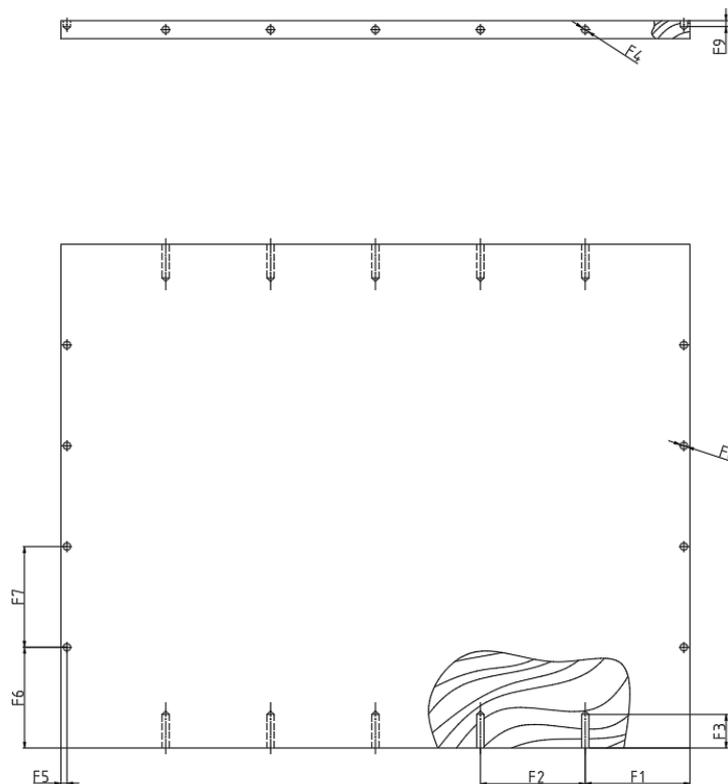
Plano Dimensionado Previo de la Base Baúl 1.1.6
